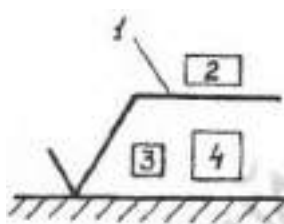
Обозначения шероховатости поверхностей.
